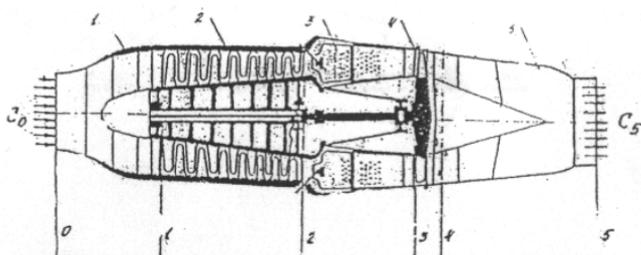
Конструктивная схема ВРД с турбокомпрессором: 1 — диффузор; 2 — центробежный компрессор; 3 — камера сгорания; 4 — газовая турбина; 5 — сопло
